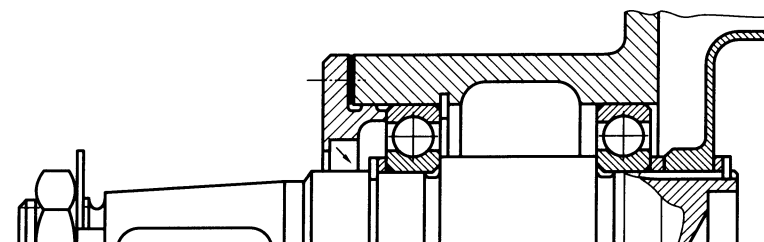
Выходной вал волнового зубчатого редуктора
